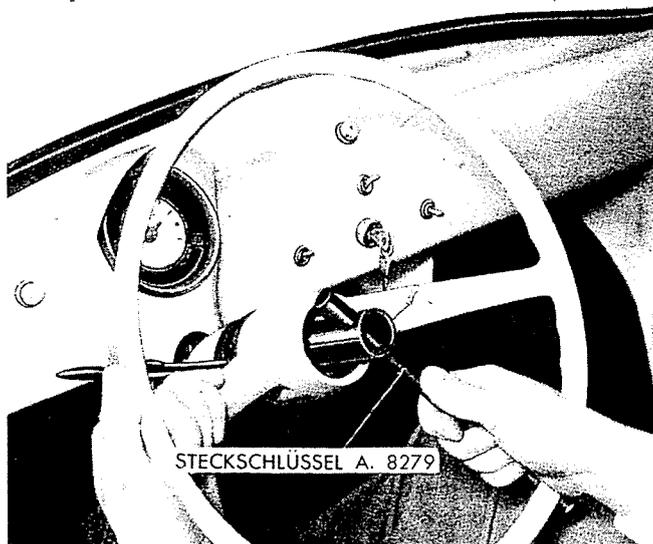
Befestigungsmutter des Lenkrads mit Schlüssel A. 8279 lösen.
